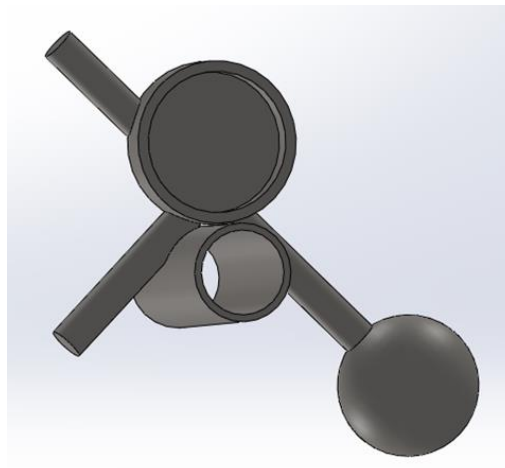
Diseño final soporte esférico con laser de cámara Propia autor.
